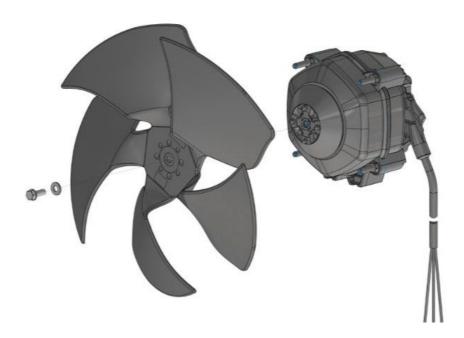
Ensamblado del ventilador (eje de rosca interna). Ajuste del par de torsión: 1.5 - 1.7 Nm
